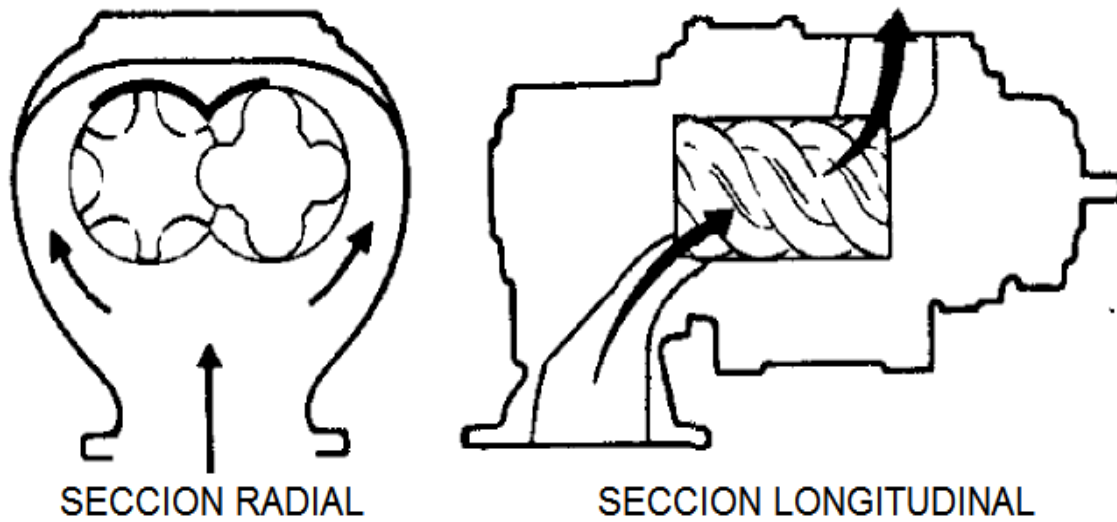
Disposición de los rotadores de un Compresor de Tornillo
